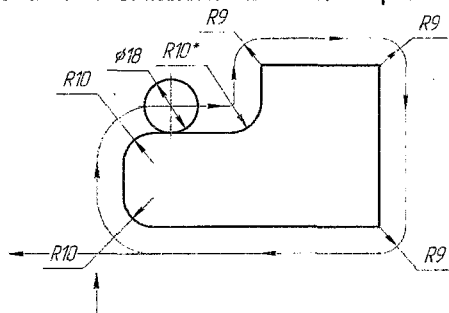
Схема выбора диаметра фрезы для чистового контурного фрезерования
